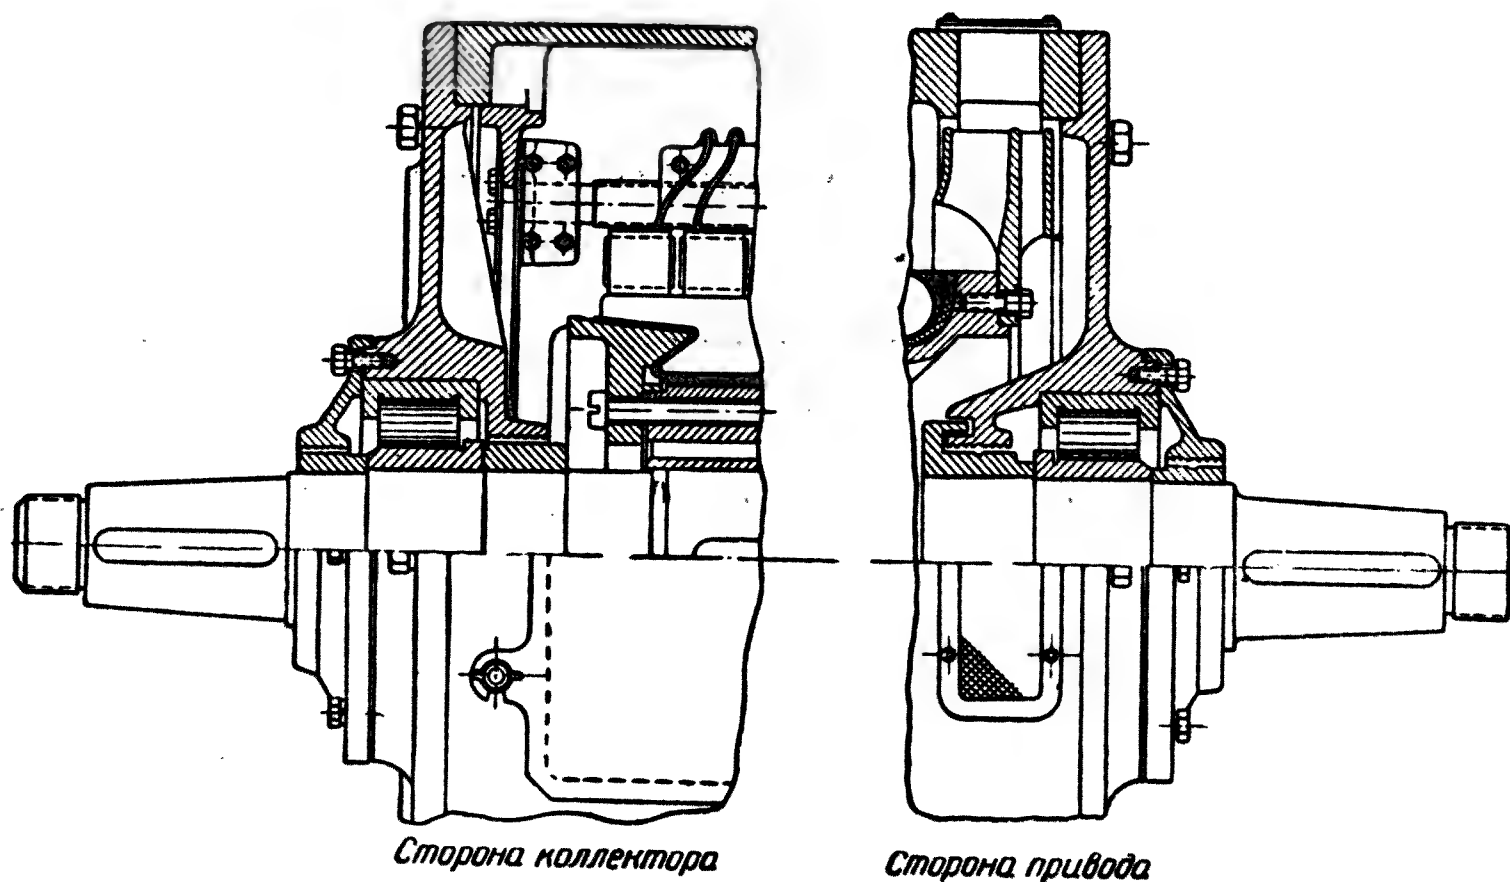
Подшипниковые узлы на роликоподшипниках.
